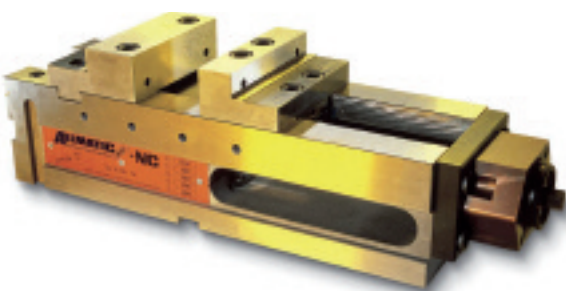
Hochdruckspanner «TC». (Bilder: Allmatic-Jakob)
